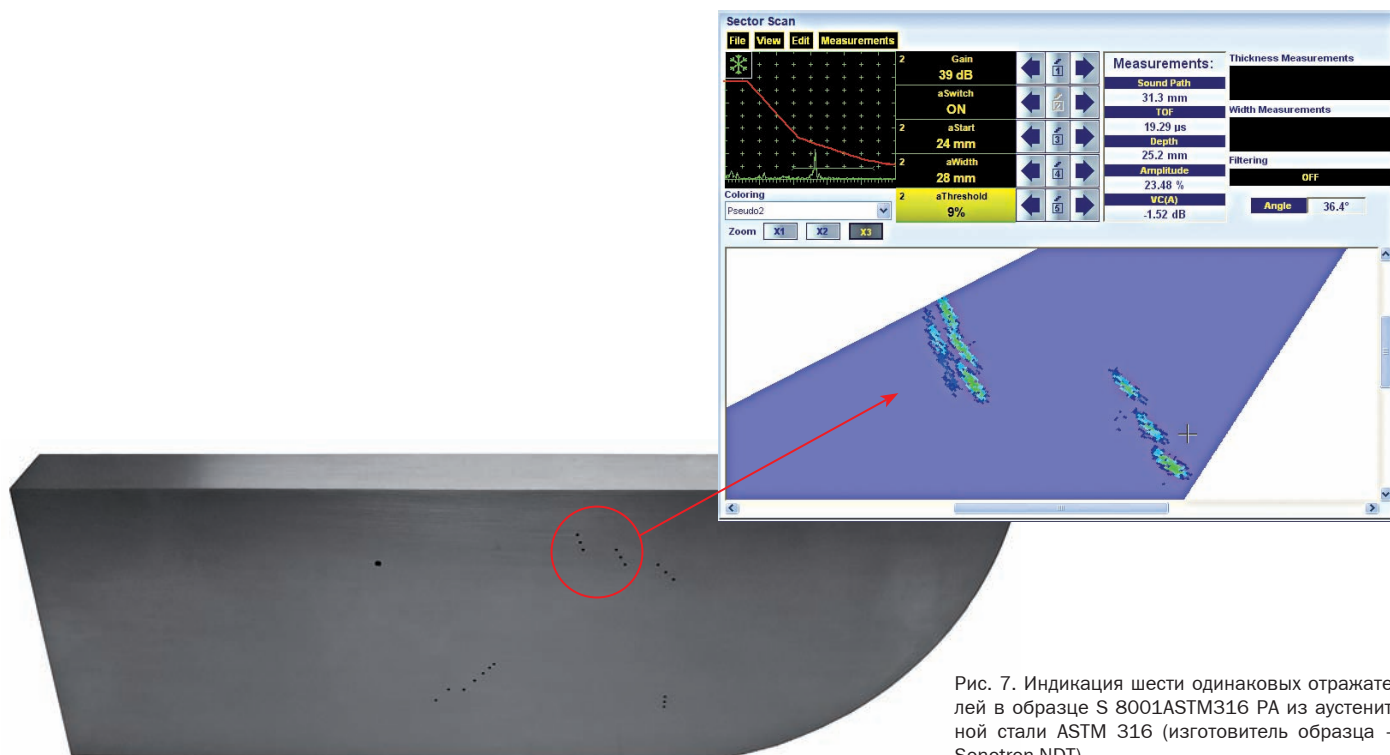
Индикация шести одинаковых отражателей в образце S 8001ASTM316 PA из аустенитной стали ASTM 316 (изготовитель образца – Sonotron NDT)
